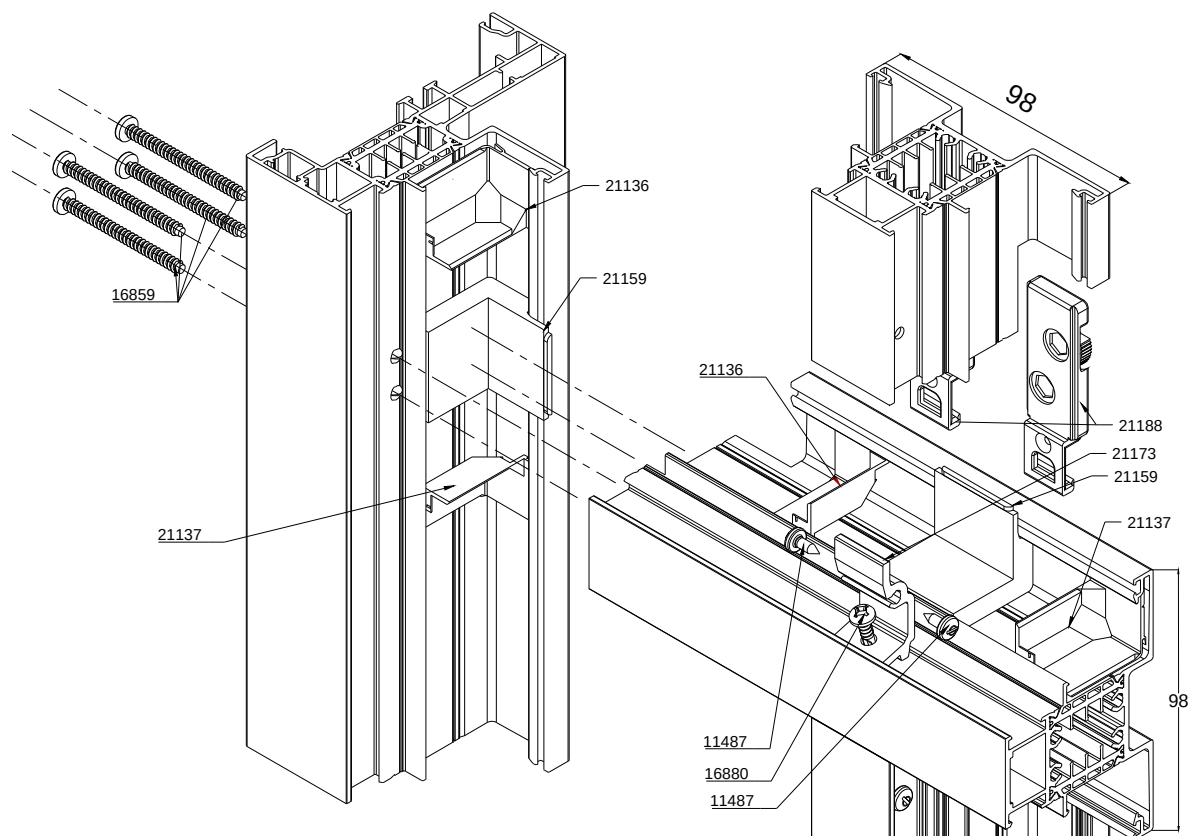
DETAILS D'ASSEMBLAGE MENEAU SUR SEUIL
